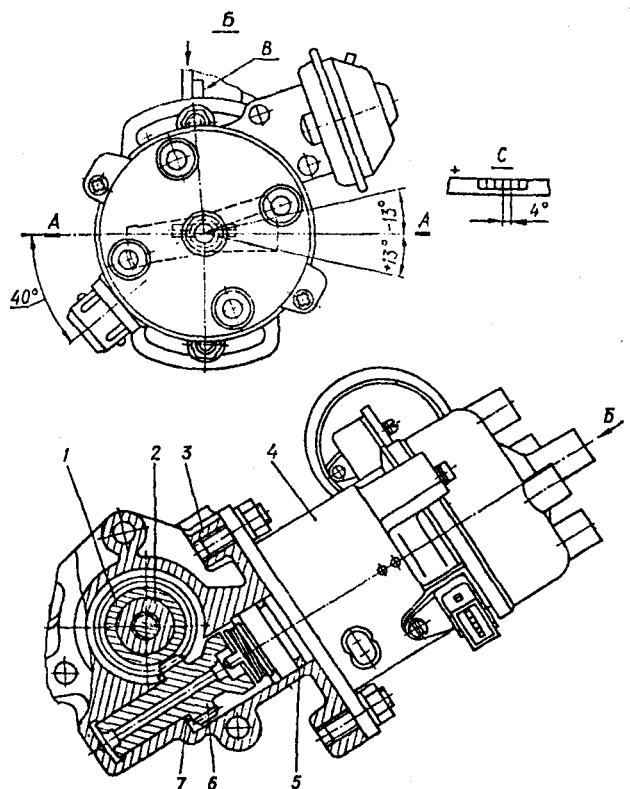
Установка датчика-распределителя зажигания: 1 – ведущая шестерня привода датчика-распределителя; 2 – распределительный вал; 3 – корпус привода распределителя и бензинового насоса; 4 – датчик-распределитель зажигания; 5 – уплотнительное резиновое кольцо; 6 – ведомая шестерня привода датчика-распределителя; 7 – упорное кольцо; В – прилив на корпусе для установки октан-корректора; А-А – ось, параллельная продольной оси двигателя
